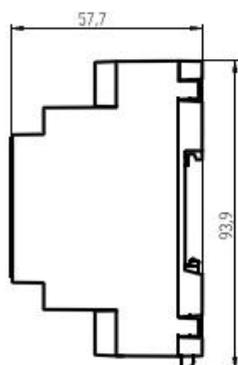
Габаритный чертеж «БРИЗ-РВ.SL»
